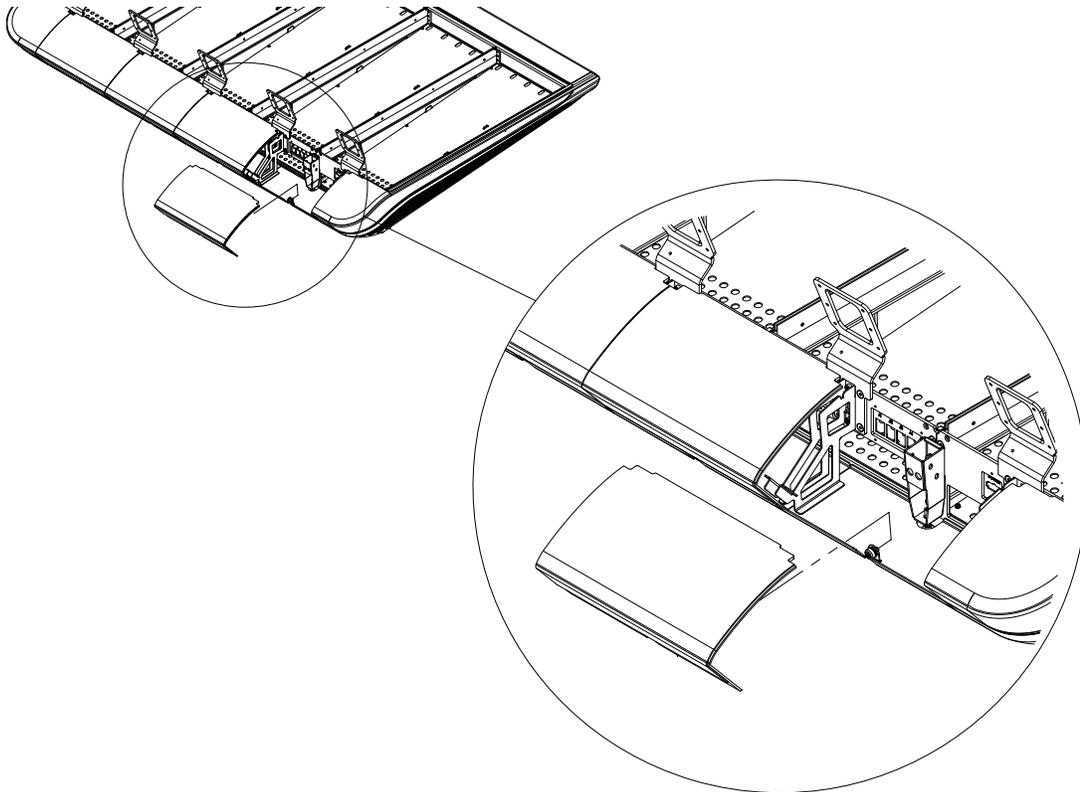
Anbringen der unteren Rückplatten (Kabel des Anzeige-Moduls nicht abgebildet)
